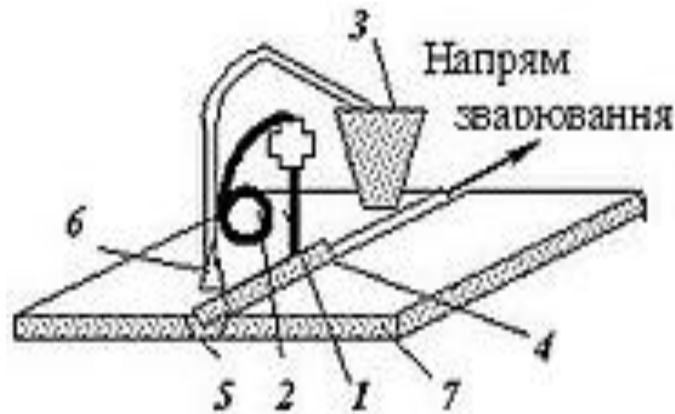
Схема автоматичного електродугового зварювання:
